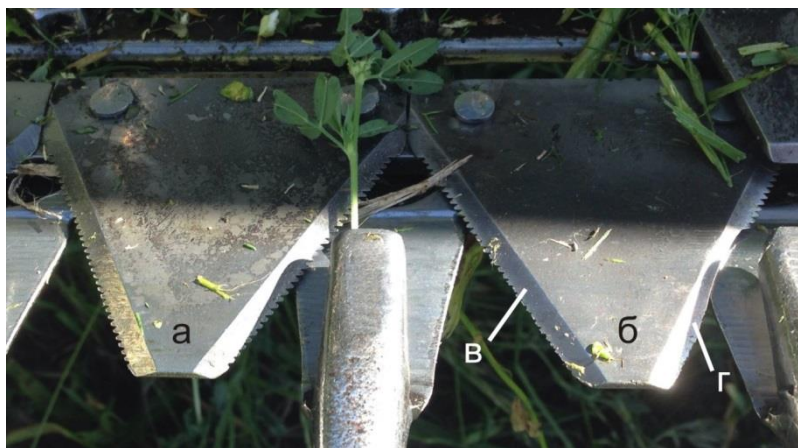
Общий вид ножей косилки после скашивания 164 га многолетних трав: а – подвергнутый ЭДТО; б – стандартный; в – режущая кромка со стороны ножа подвергнутого ЭДТО; г – режущая кромка со стороны стандартного ножа
